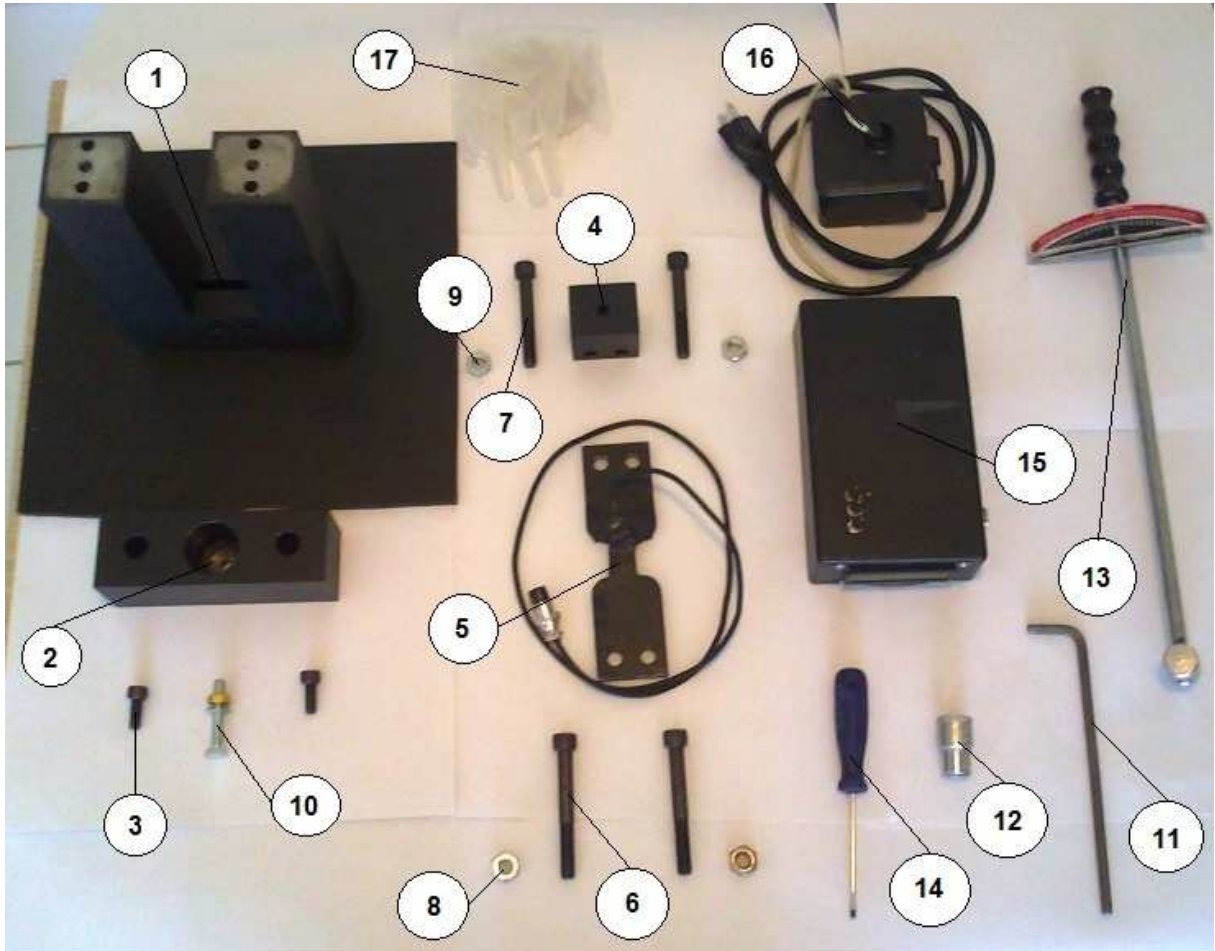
Conjunto de peças para montagem do dispositivo de medição
